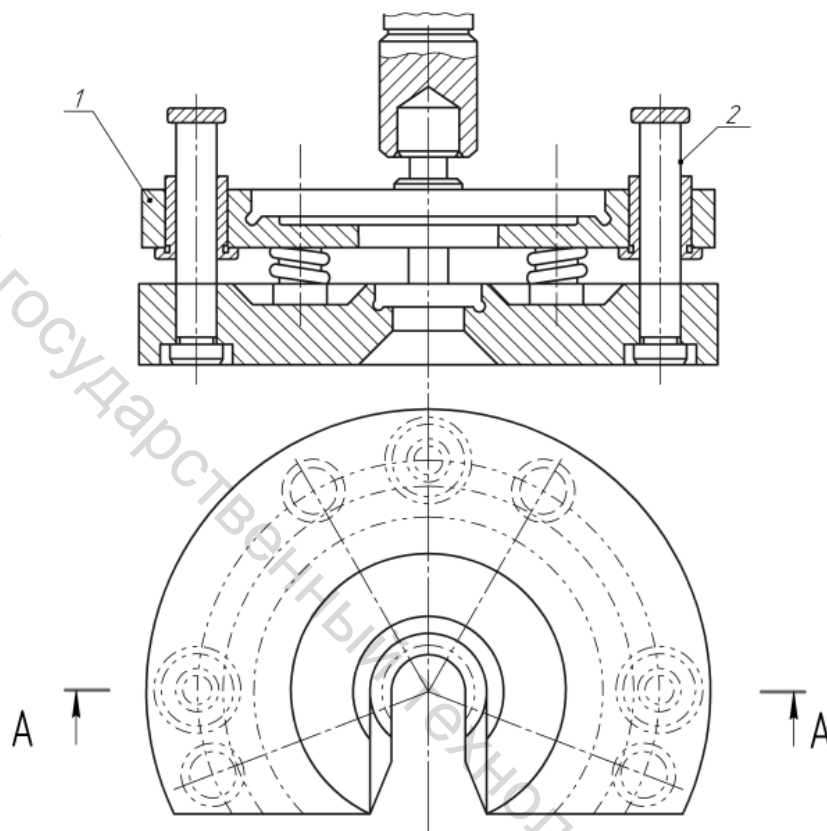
Напрессовка зубчатых колес на вал при помощи прессы и приспособления
